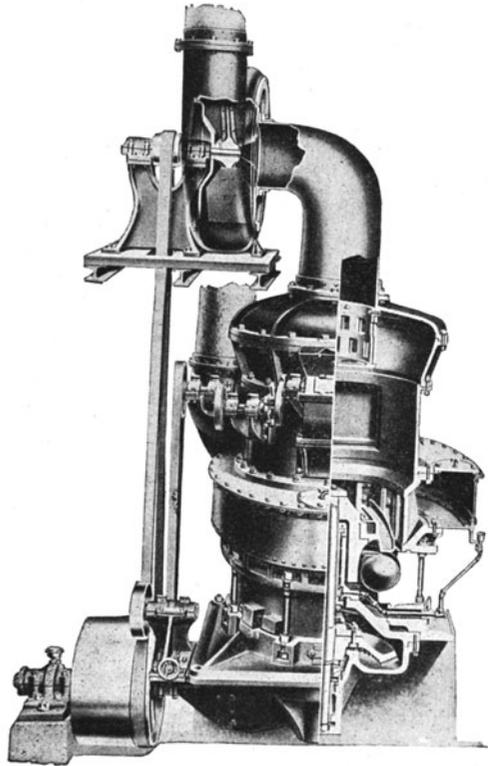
Fuller-Kugelmühle mit Windsichtung von Claudius Peters, Hamburg.
